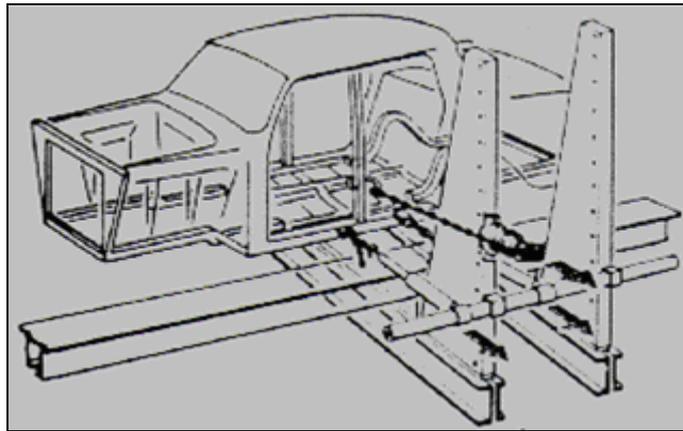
Automóvil colocado sobre la plataforma de enderezar a fin de estirarlo para ello se utiliza una de las columnas.
